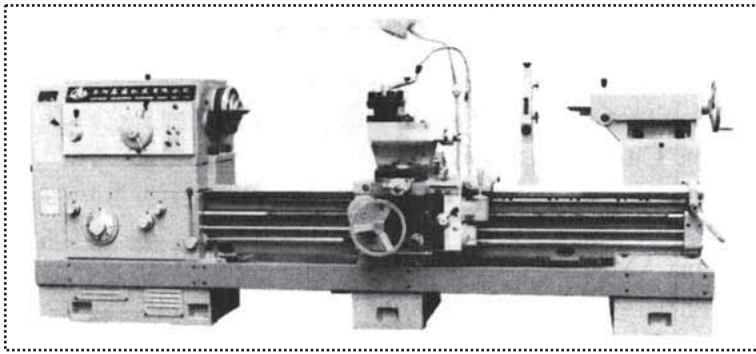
Универсальный токарно-винторезный станок мод. 1N65B
